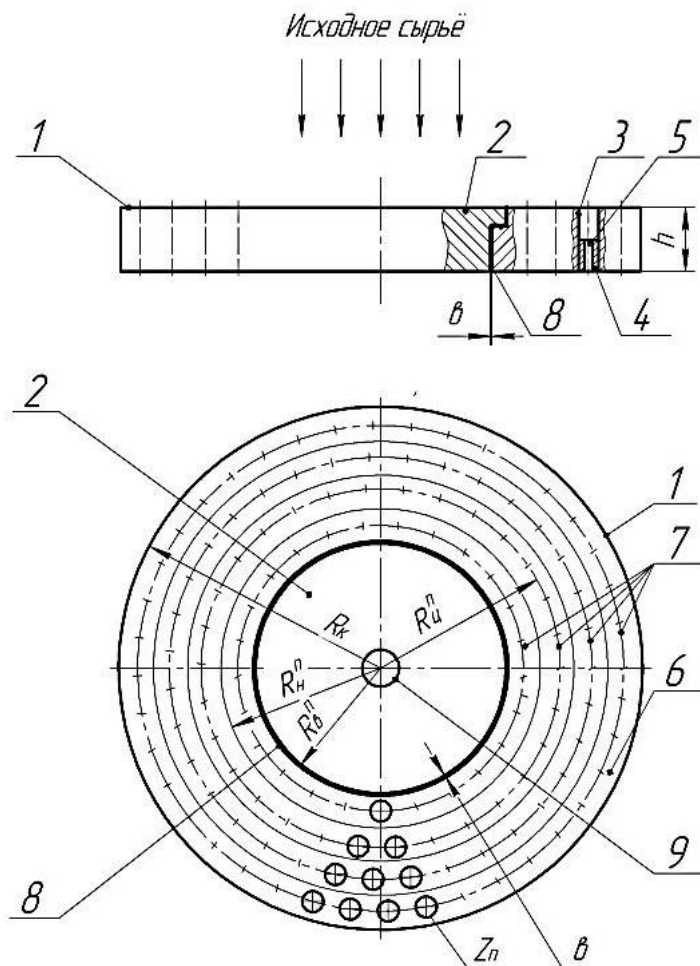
Принципиально-конструктивная схема составной матрицы для производства макаронных изделий: 1 – корпус матрицы; 2 – основание; 3 – колодцы; 4 – вкладыши; 5 – формующие отверстия; 6 – кольца условные; 7 – окружности цилиндрические; 8 – зазор; 9 – отверстие центральное; 10 – выступ; R_k – радиус корпуса матрицы; R_n^n – центральный радиус n -го условного кольца; R_n^n – наружный радиус n -го условного кольца; R_n^n –
